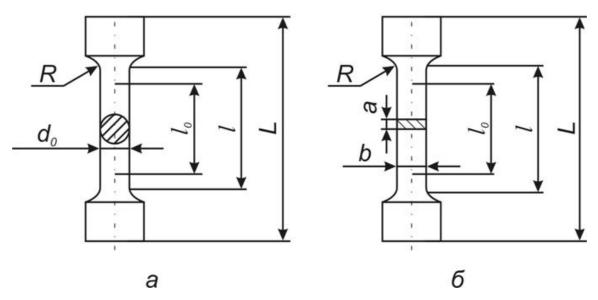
Образцы для испытаний: a — круглый образец; δ — плоский образец; L — общая длина; l — рабочая длина; l_0 — начальная расчетная длина; d_0 — диаметр образца до испытания; a — толщина; b — ширина; R — радиус скругления.
